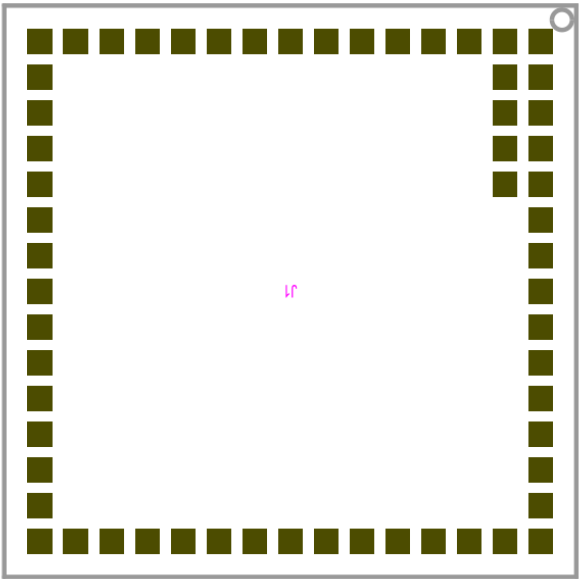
BOT 面（接口焊盘面 Pad Side）
